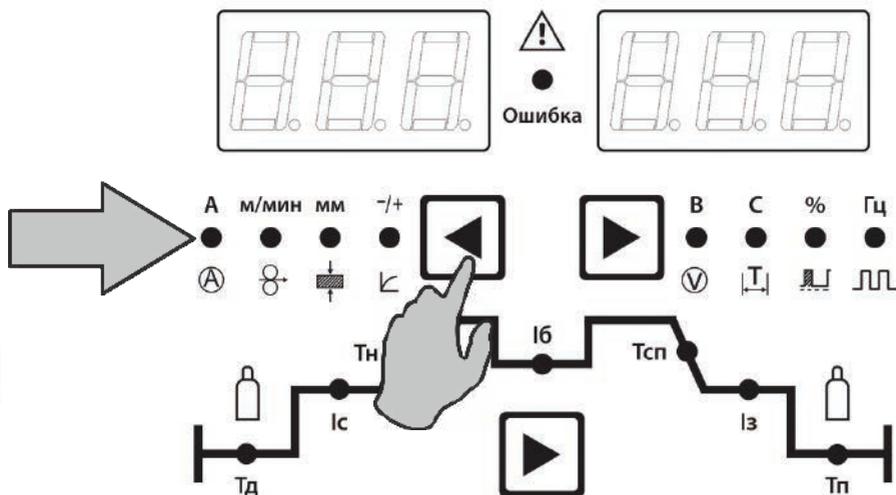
Установка времени продувки газом до сварки.
